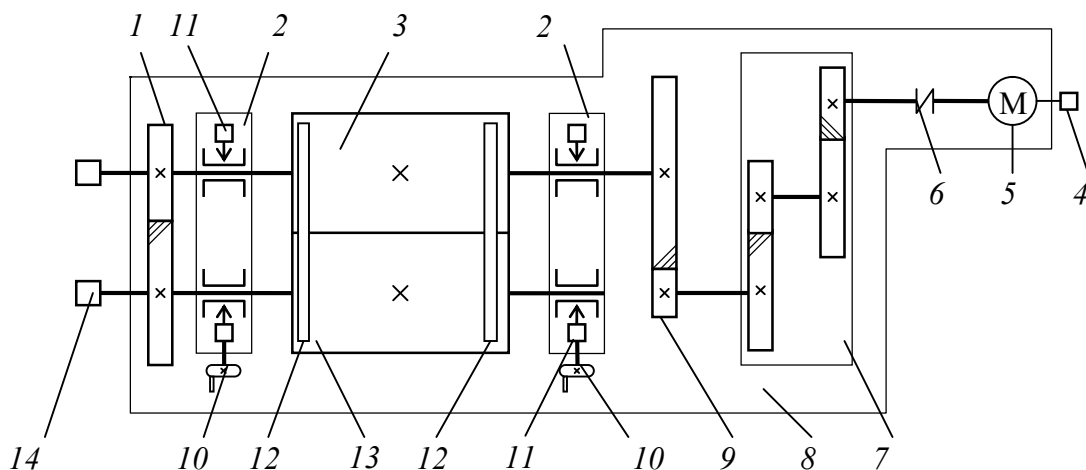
Схема валкової установки: 1 – фрикційні шестерні; 2 – стійки; 3 – задній валок; 4 – тахогенератор; 5 – електродвигун; 6 – муфта; 7 – редуктор; 8 – зварна основа; 9 – зубчаста передача; 10 – механізми переміщення переднього валка; 11 – месдоза; 12 – обмежувальні стріли; 13 – передній валок; 14 – колектор підведення електричного струму до нагрівників валка
